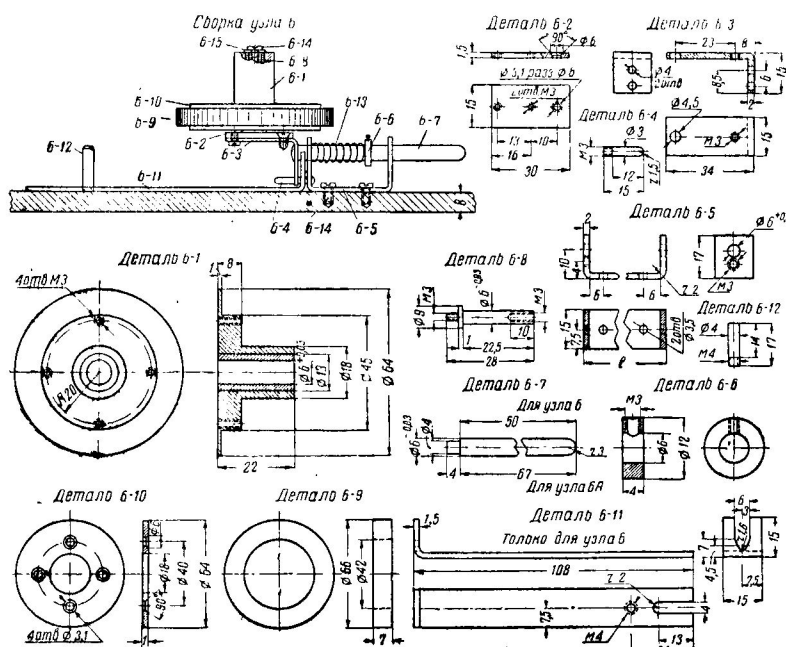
Паразитный ролик рабочего хода (узел 6) и перемотки (узел 6А) и его детали: 6-1—корпус ролика (дюралюминий Д16Т)—1 шт.; 6-2—подвижная площадка (сталь 20)—1 шт.; 6-3—уголок (сталь 20)—1 шт.; 6-4—направляющий стержень (сталь 45)—1 шт.; 6-5—скоба (сталь 20)—1 шт.; для узла 6 $l=32$ мм и для узла 6А $l=65$ мм; 6-6—кольцо стопорное (сталь 25)—1 шт.; 6-7—стержень (сталь 45)—1 шт.; 6-8—ось паразитного ролика (сталь У8А)—1 шт.; 6-9—кольцо резиновое—1 шт.; 6-10—кольцо (дюралюминий Д16Т)—1 шт.; 6-11—вилка (сталь 20)—1 шт.; 6-12—упор (сталь 45)—1 шт.; 6-13—пружина диаметром 6,5 мм и длиной 45 мм (28 витков проволоки марки Н диаметром 0,5 мм)—1 шт.; 6-14—винт $M3 \times 6$ мм (сталь 3)—8 шт.; 6-15—шайба (сталь 3)—1 шт. Указанные количества деталей относятся к одному узлу (6 или 6А)
